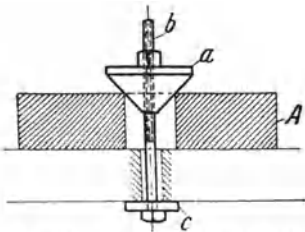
Spannung im Mittelloch des Bohrmaschinentisches.
